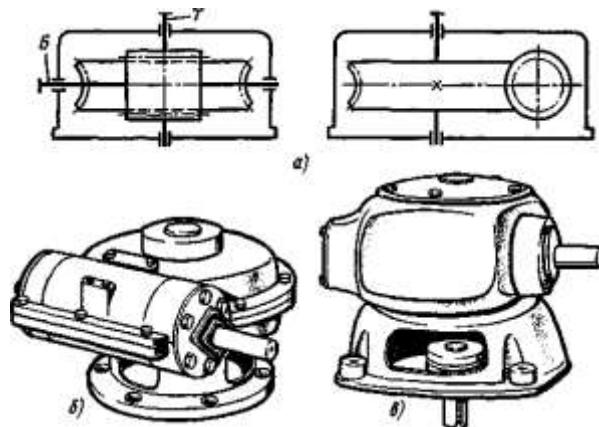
Червячный редуктор с вертикальным валом червячного колеса:
